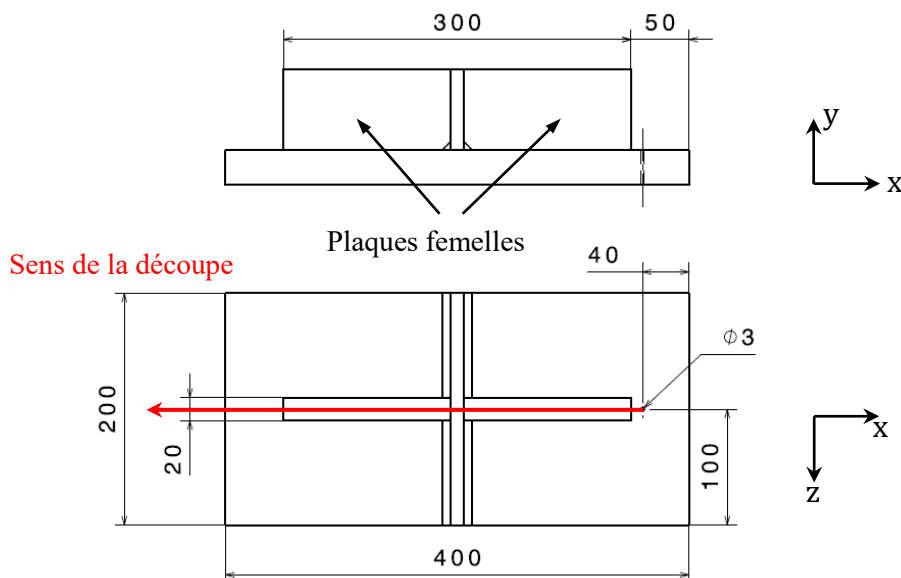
Ajout des plaques femelles pour la découpe par électroérosion - dimensions en (mm)
